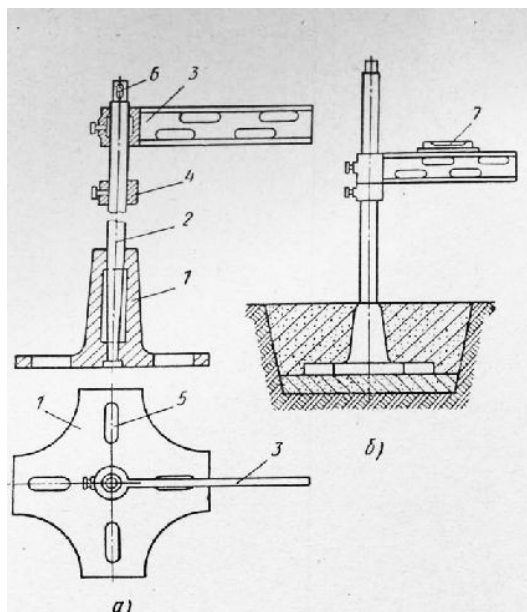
Приспособления для формовки по шаблону (а) и схема их установки (б).
